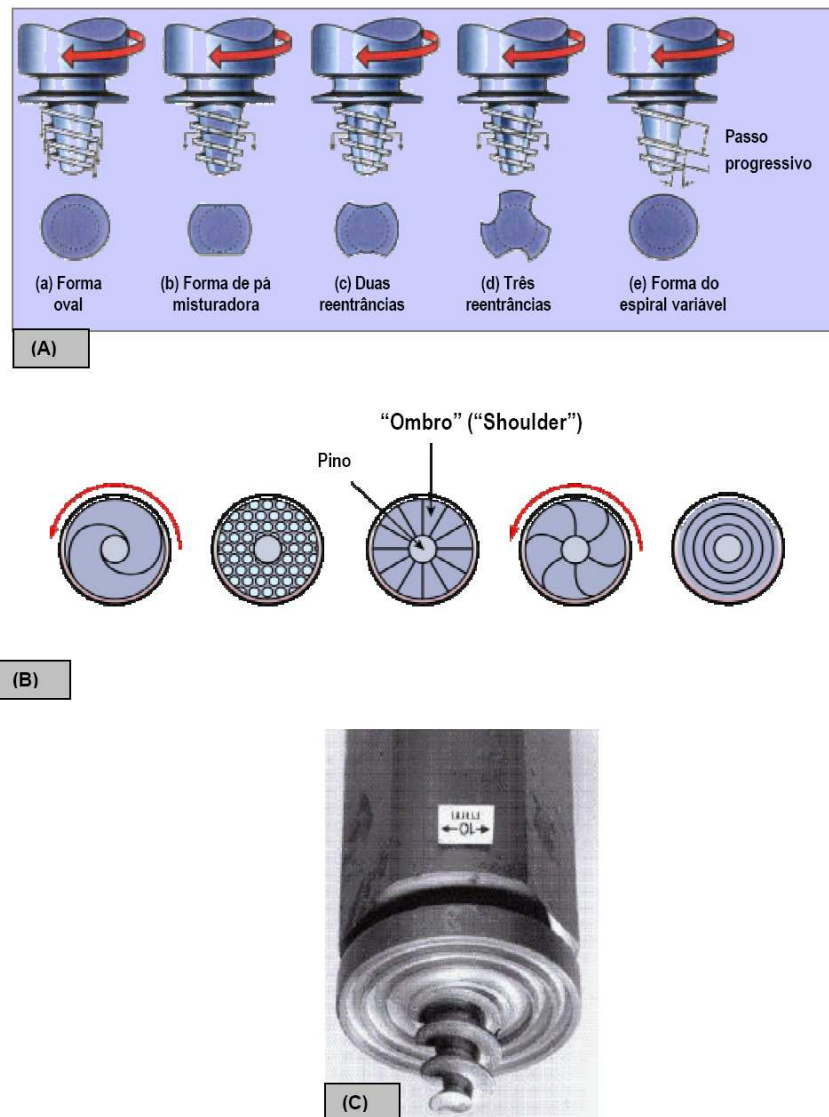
Exemplo dos diversos tipos de configurações de pinos (A) e “ombro” (B) de uma ferramenta do tipo Whorl™ utilizável na soldagem “Friction Stir Welding” das ligas da série 5XXX [Júnior, 2003].
